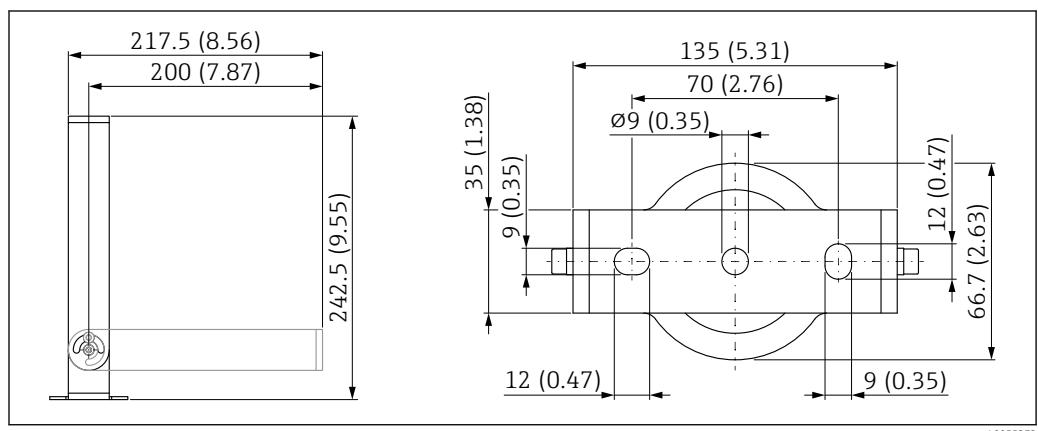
Dimensioni della staffa di montaggio. Unità di misura mm (in)
